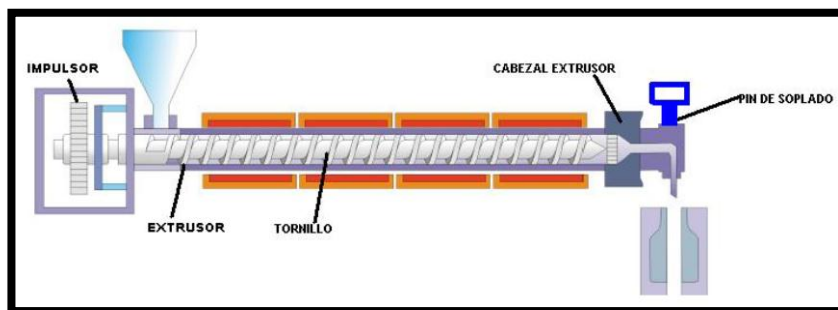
Partes constitutivas de una máquina de extrusión – soplado
